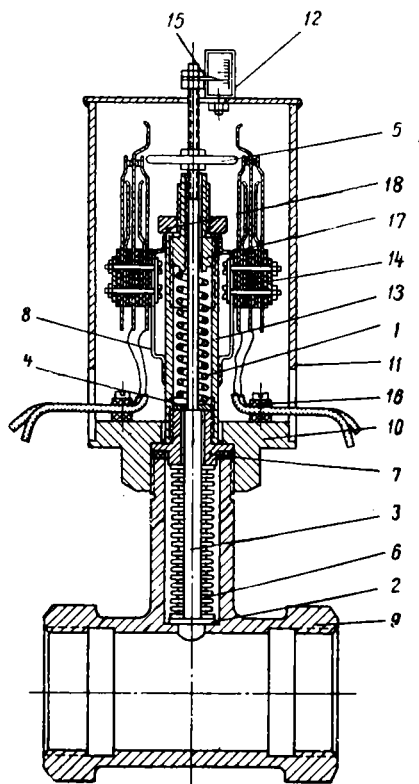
Струйное реле типа РС-ЦНИИ: 1—возвратная пружина; 2—клапан; 3—шток; 4—поршень; 5—замыкатель; 6—гофрированная трубка; 7—шток клапана; 8—направляющая планка; 9—корпус реле; 10—опорная гайка; 11—кожух; 12—шкала; 13—трубка; 14—контактные группы; 15—указательная стрелка; 16—ограничительная гайка
